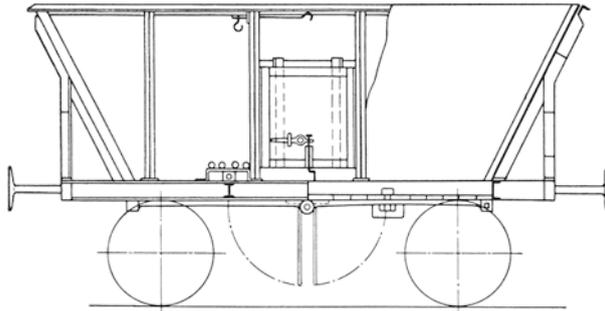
Eiserner Trichterwagen (Bodenentleerer, sog. Saarbrückener Trichterwagen), Längsansicht.
